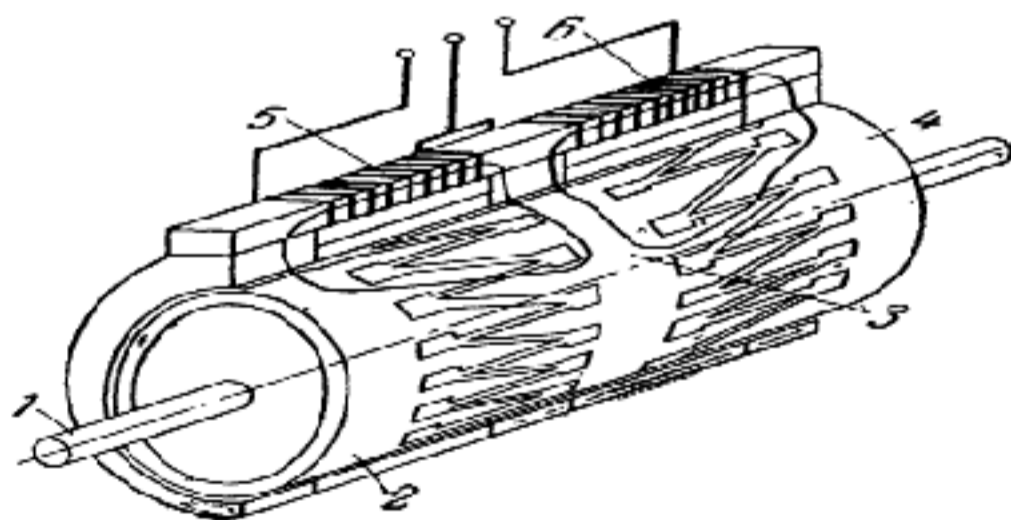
Прилад для вимірювання обертального моменту індуктивного типу, [46].
